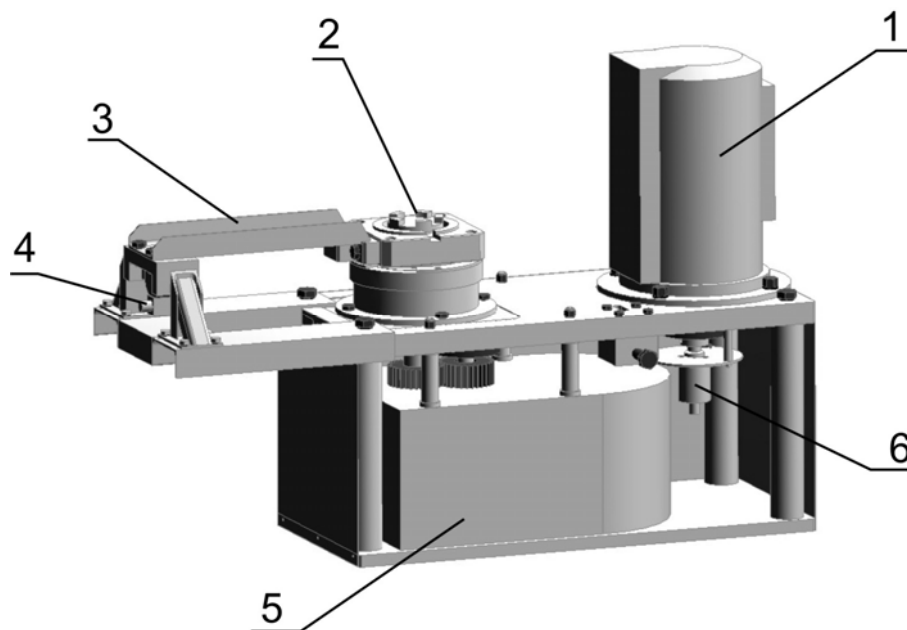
Внешний вид испытательного стенда для нагрузочных испытаний
